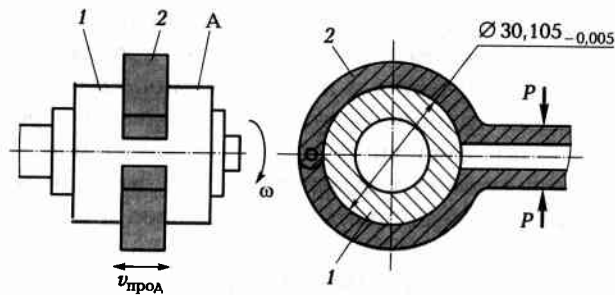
Схема притирания наружной цилиндрической поверхности
